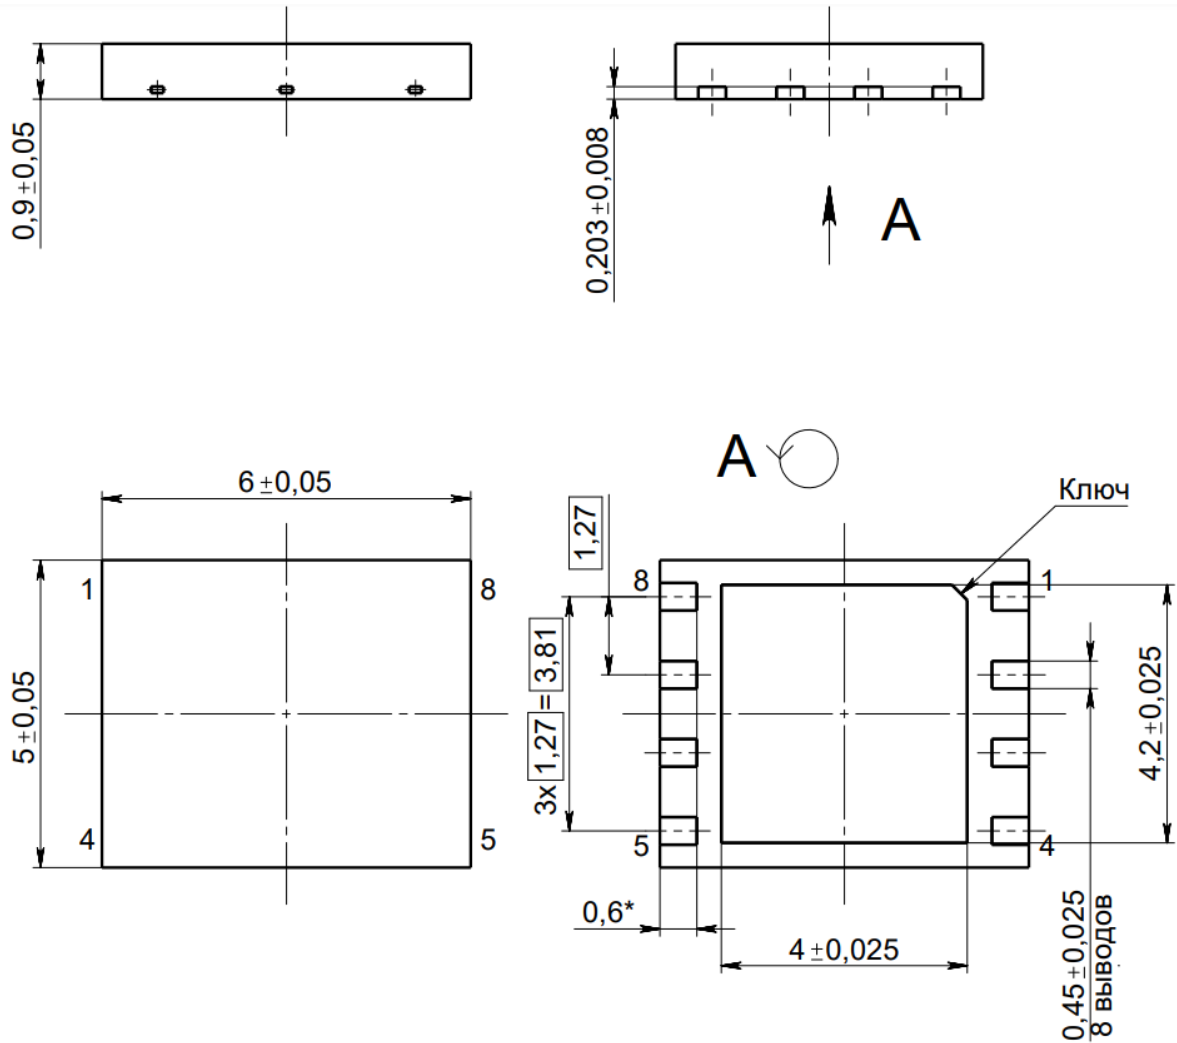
Габаритный чертеж корпуса DFN600X500X90-8 (размеры в мм)
